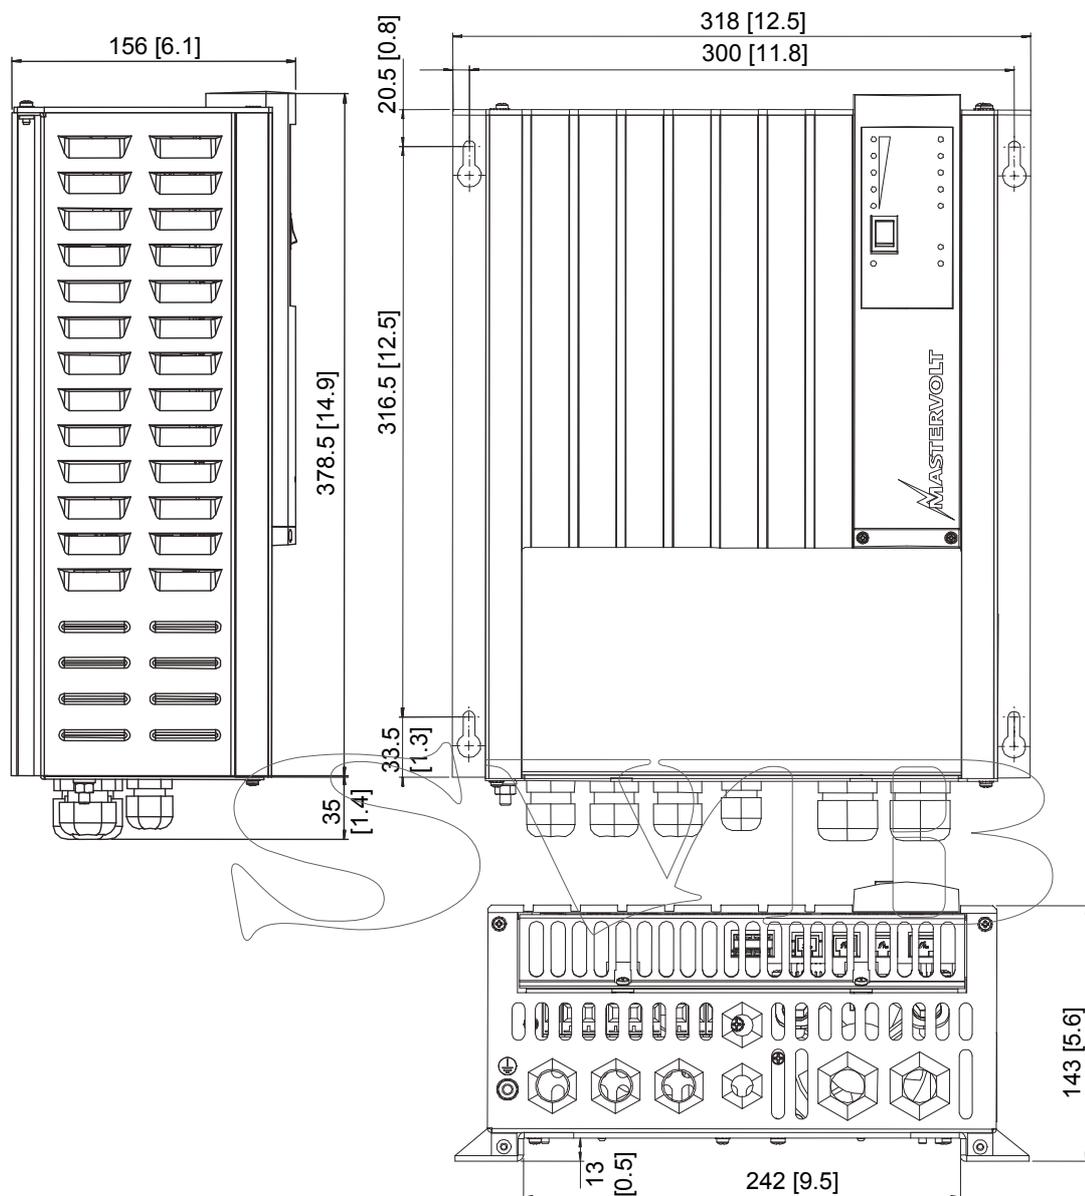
Dimensiones en mm [inch] del Mass Combi 12/1600-60 y 24/1800-35
